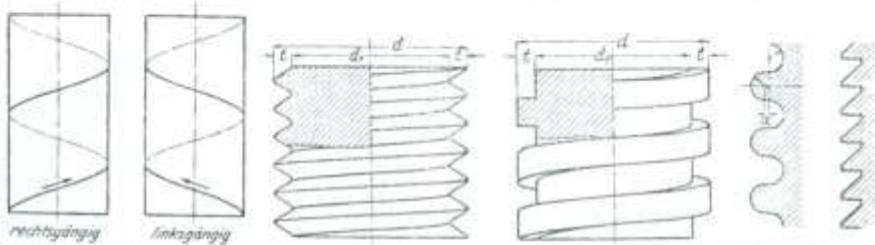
Rechts- und linksgängige Schraubenschnitte.
